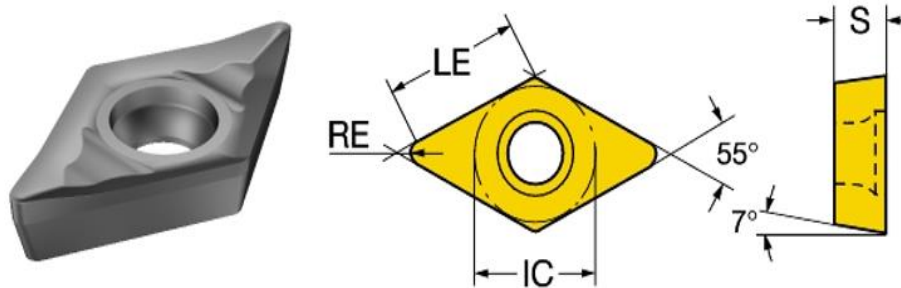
Herramienta de corte DCGX 11T304-AL H10 [22].
